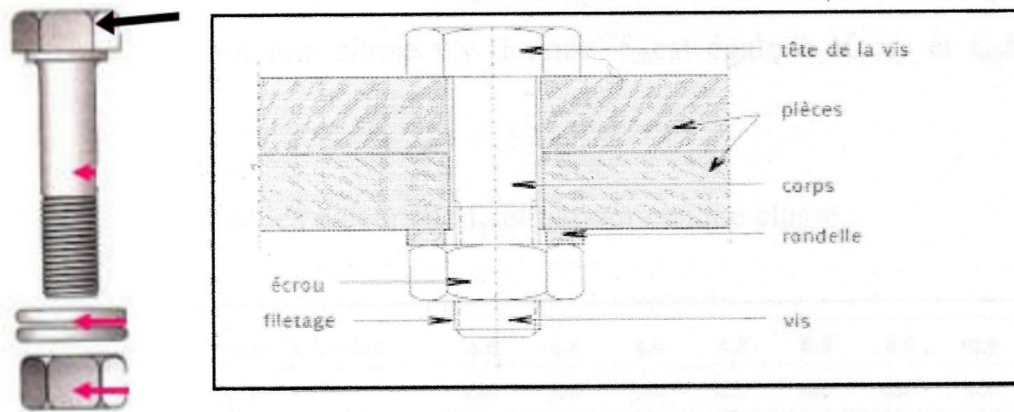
Schéma explicatif d'assemblage de deux pièces par boulon
